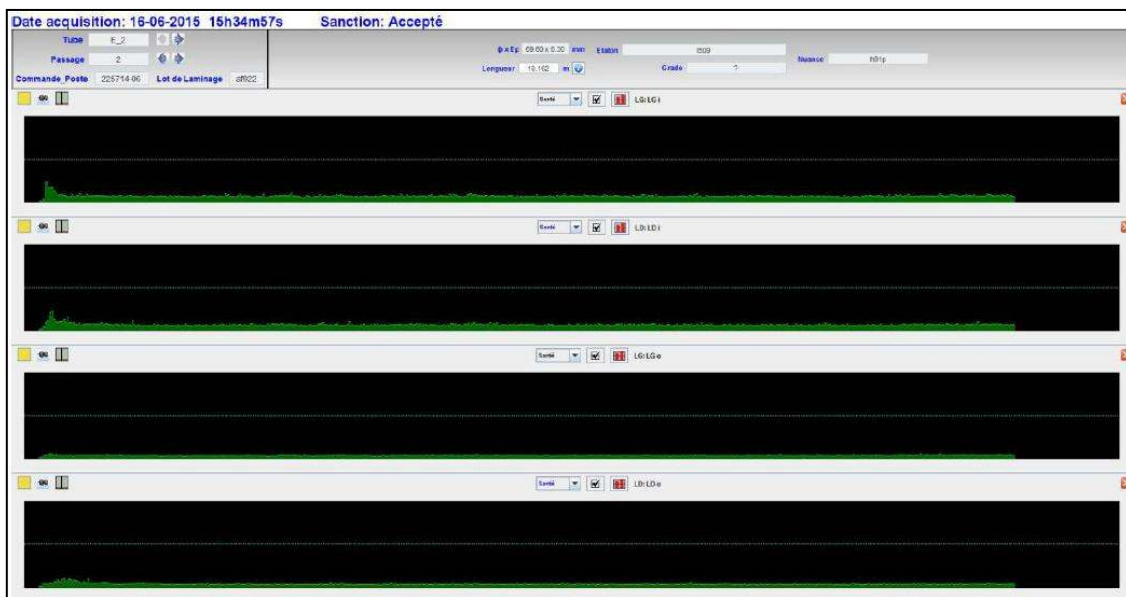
Inspection d'un tube de production – sans défaut – sur Lineview
